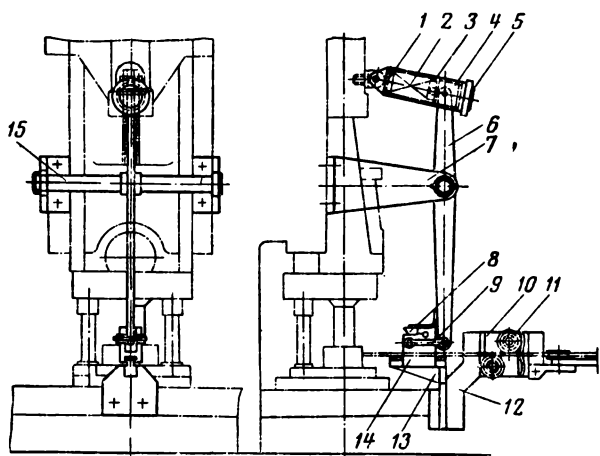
Пресс для штамповки коллекторных пластин.
